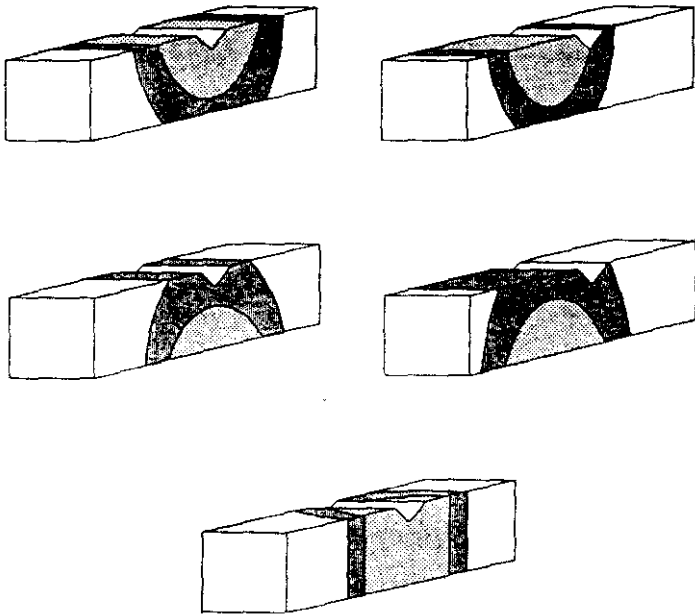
Probeta Charpy Mostrando Diferentes Localizaciones de la Entalla Respecto al Perfil del Cordón de Soldadura.
